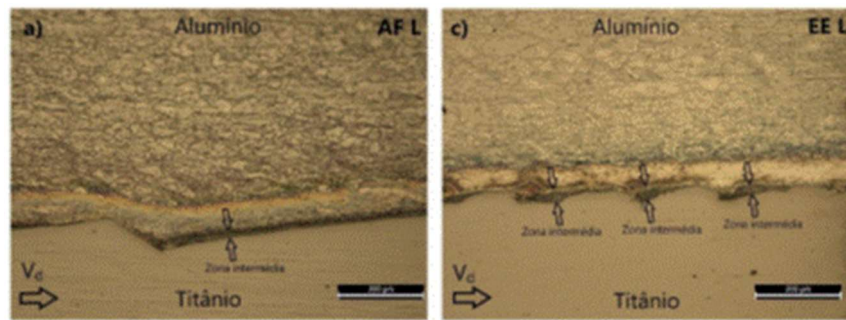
Microscopia ótica de cortes longitudinais à direção de soldadura das soldaduras: (a) utilização de ANFO; (c) utilização de uma emulsão explosiva com 2% de EPS [24].
